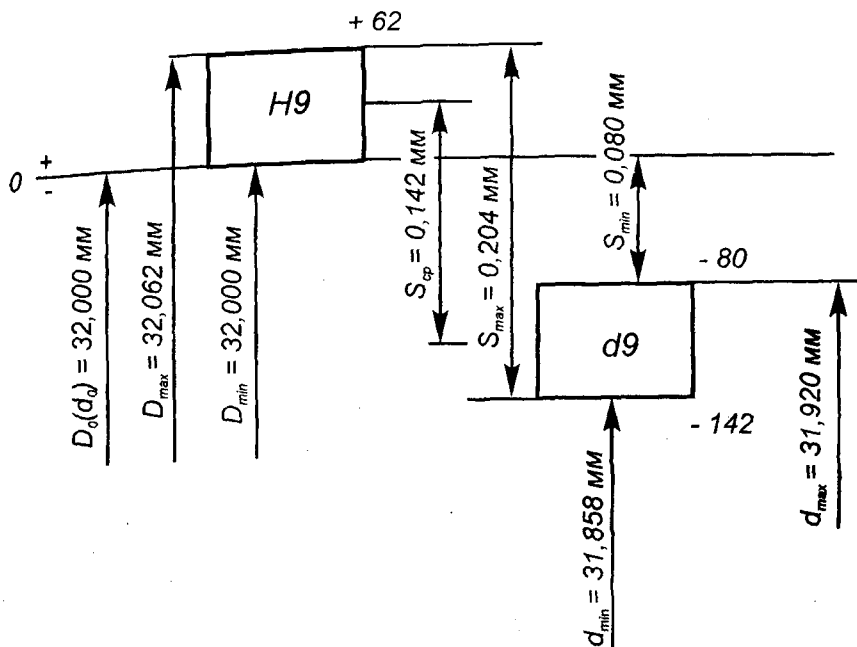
Схема расположения полей допусков вала и втулки
